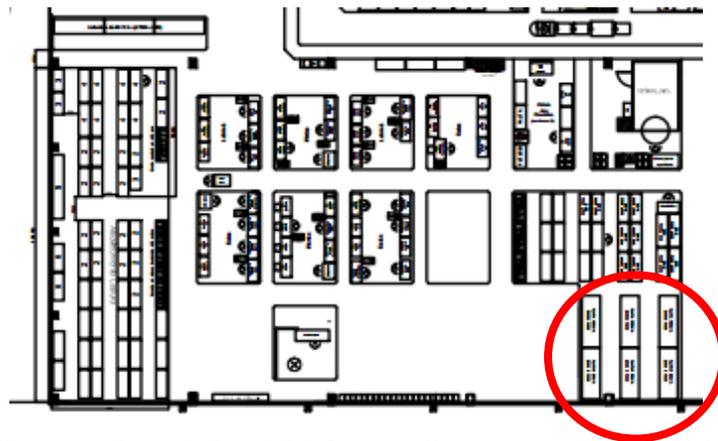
Zona de Stock PA Costura (Supermercado de Apoio).
